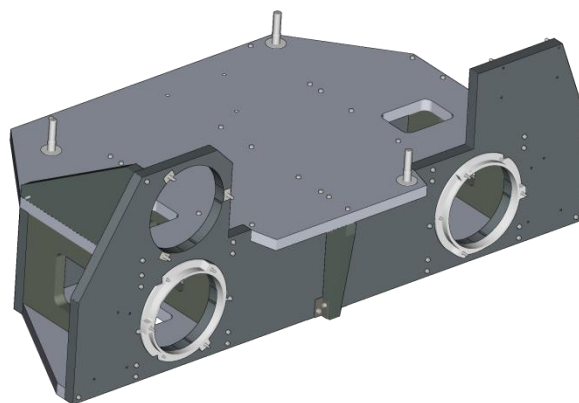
Общий вид корпуса блока полезной нагрузки КА "Січ-2М"
